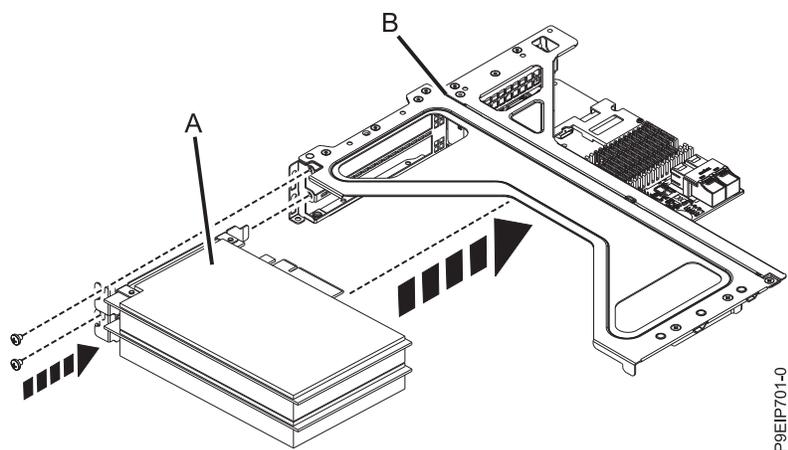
Inserción de un adaptador a PCIe en la posición 2 o 3 de la tarjeta de expansión PCIe
